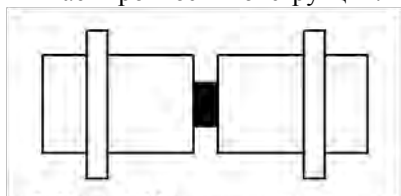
Эскиз ДМР с цилиндрическими модулями
